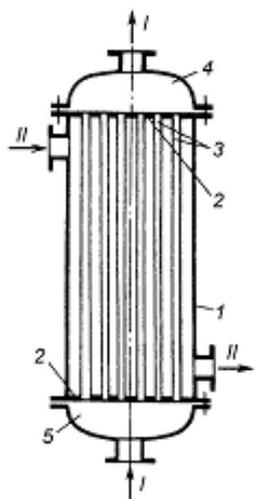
Кожухотрубчатый теплообменник: - корпус (кожух); 2- трубные решетки; 3- трубы; 4- крышка; 5- днище; I, II – потоки теплоносителей
